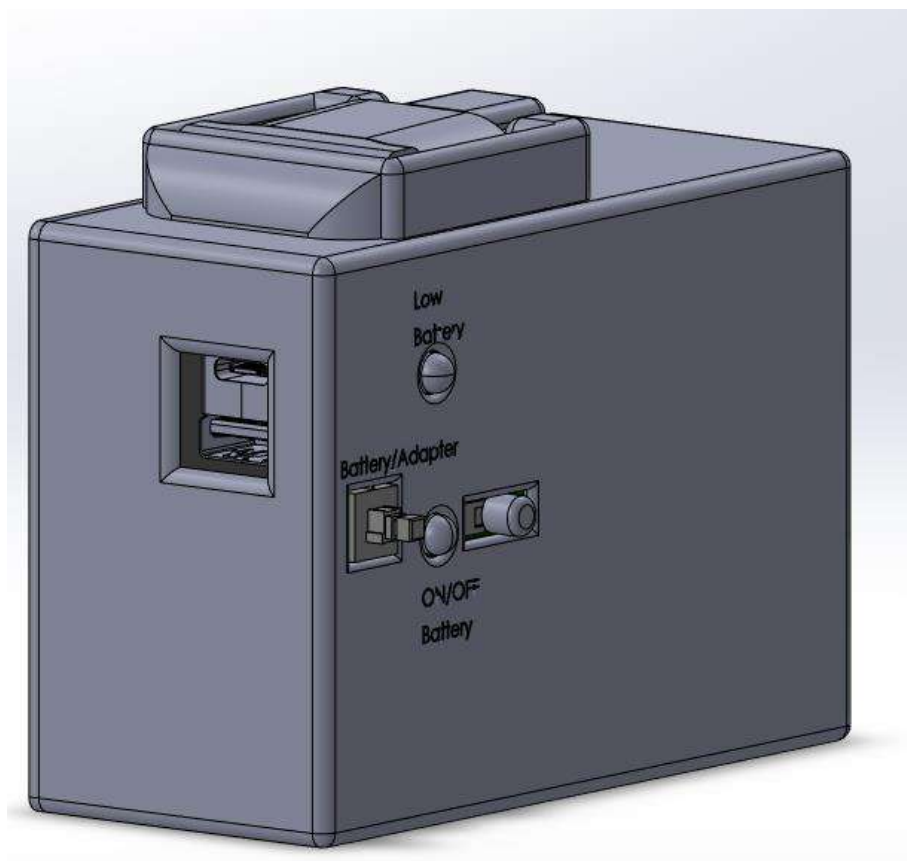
Вигляд корпусу спереду та з опущеною вилкою зарядки
